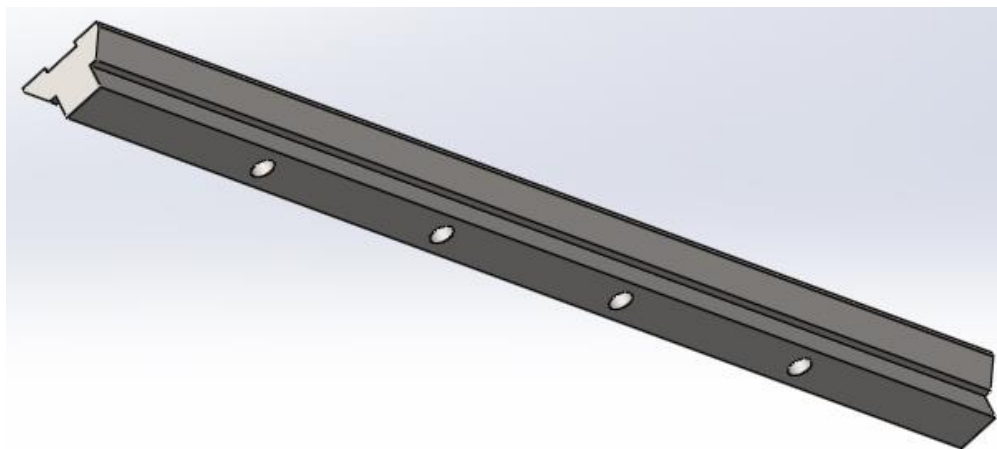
Охватываемая направляющая с отверстиями для болтового соединения
